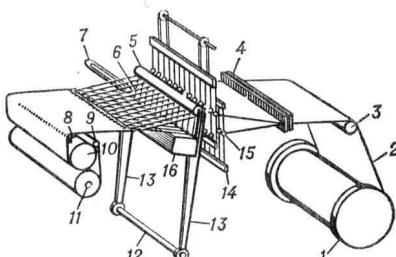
Принципиальная схема образования ткани на ткацком станке: 1 — навой; 2 — нити основы; 3 — скос; 4 — ламели; 5 — вершин; 6 — бёрдо; 7 — челнок; 8 — грудница; 9 — направляющий валик; 10 — вальян; 11 — товарный валик; 12 — подбатаный вал; 13 — лопасть батана; 14 — ремизка; 15 — глазок галевы; 16 — батан.
